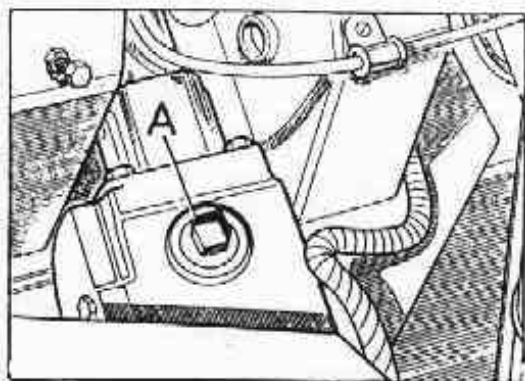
Tapón de llenado de la caja de engranajes de la dirección.
